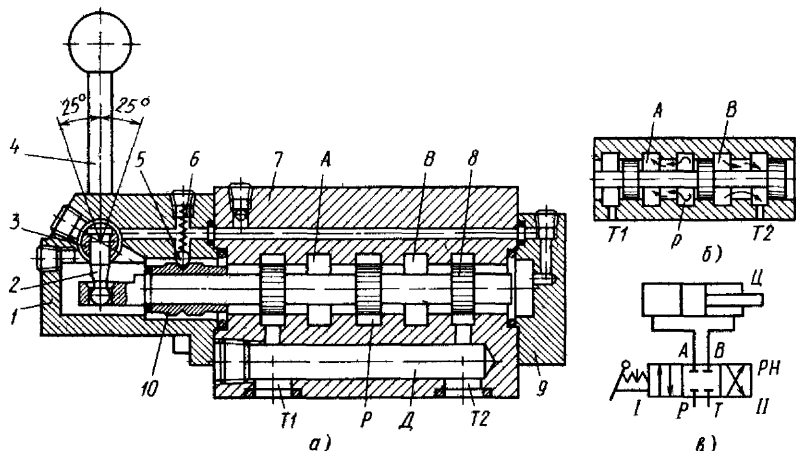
Направляющий золотниковый распределитель 4/3 типа ПГ74-24М с ручным управлением:
